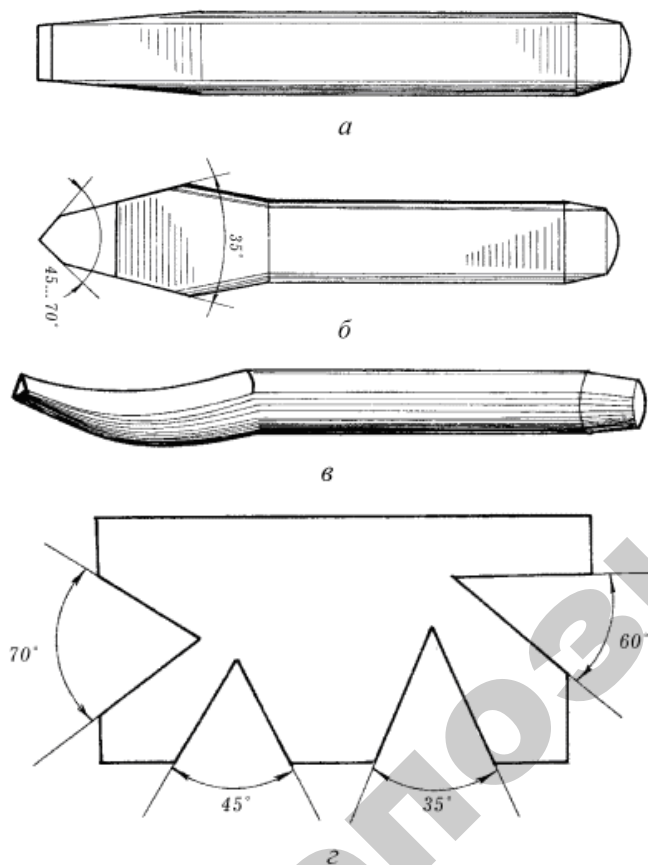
Рубящий инструмент: а – зубило слесарное; б – крейцмейсель; в – канавочники; г – шаблон для контроля заточки
